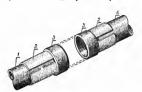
Подготовка камеры к стыковке: 1 — камера; 2 — разрезные манкеты; 5 — поверхности последующей шероховки; 4 — вставка.
